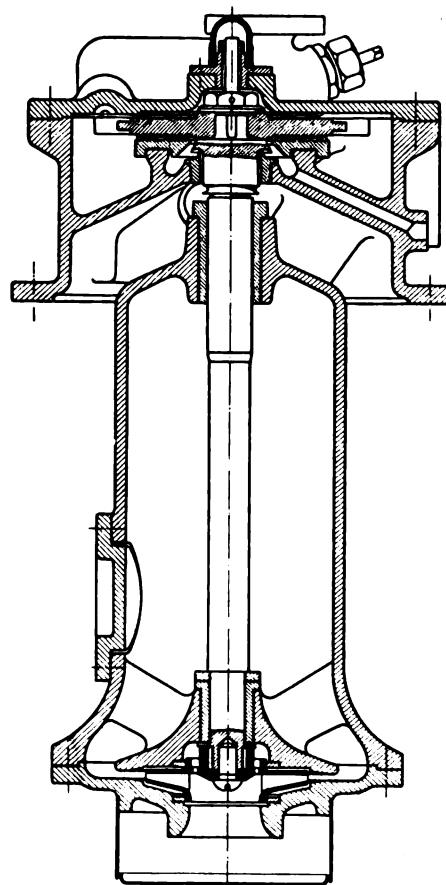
General Electric Co., Ltd., Hilfsölpumpe mit Turbinenantrieb.
